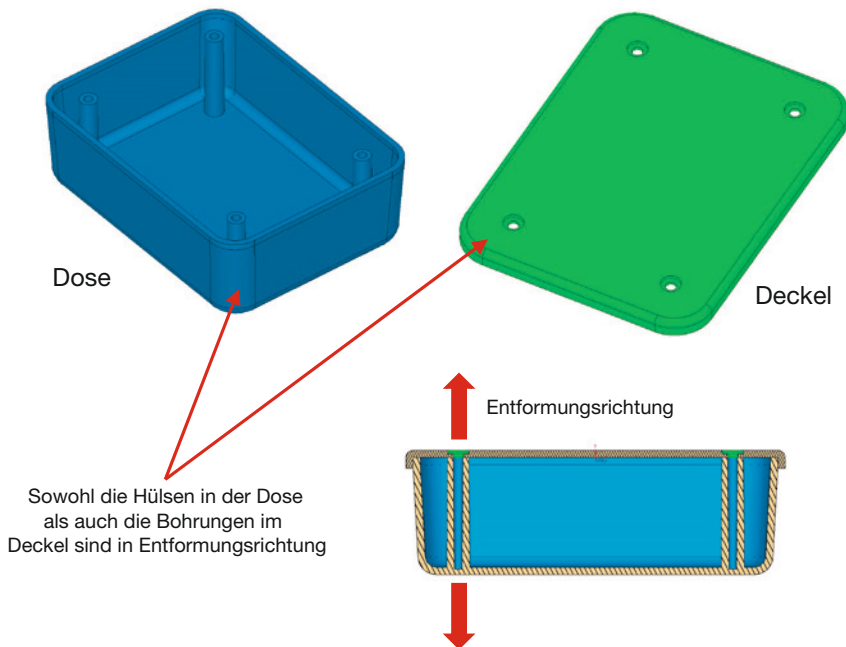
Teile für ein Auf-Zu-Werkzeug mit zusätzlichen Elementen
